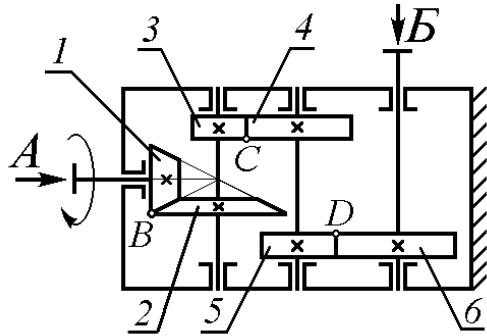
Триступінчастий конічно-циліндричний редуктор
